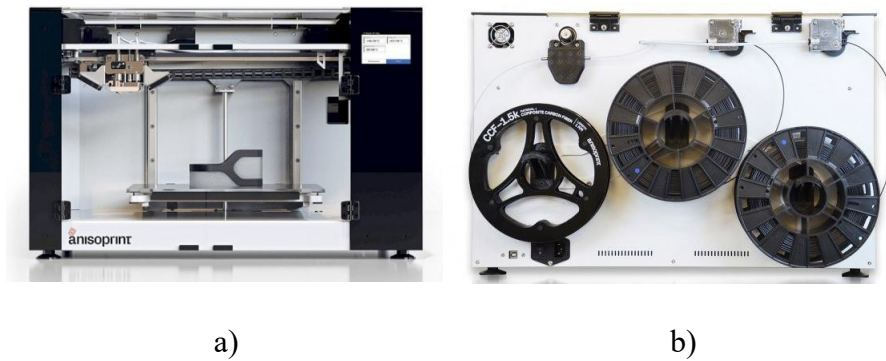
a) Fronte e b) retro della stampante Composer A3 Anisoprint
